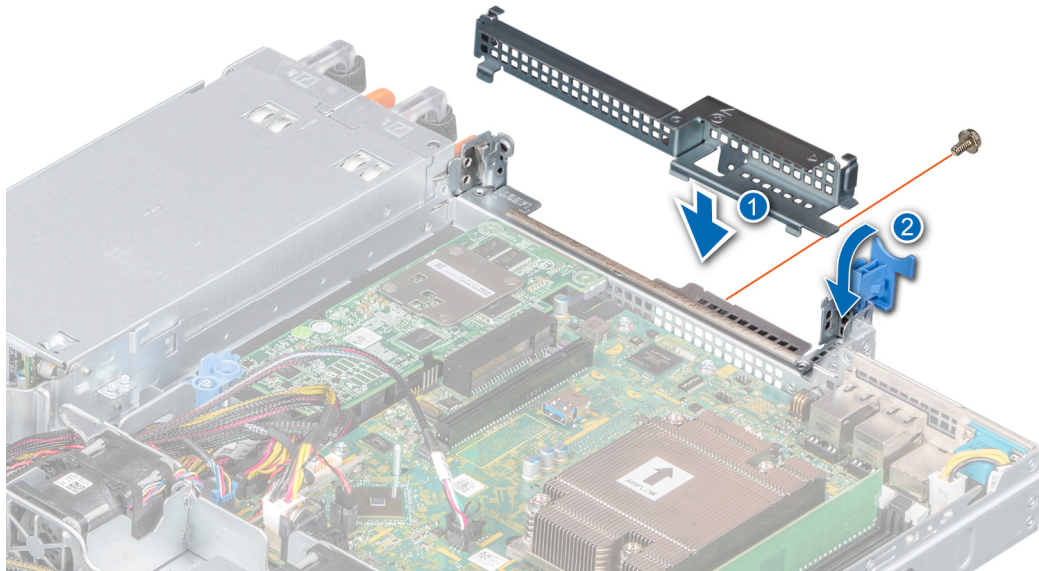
Installation de la plaque de recouvrement de carte de montage pour carte d'extension
